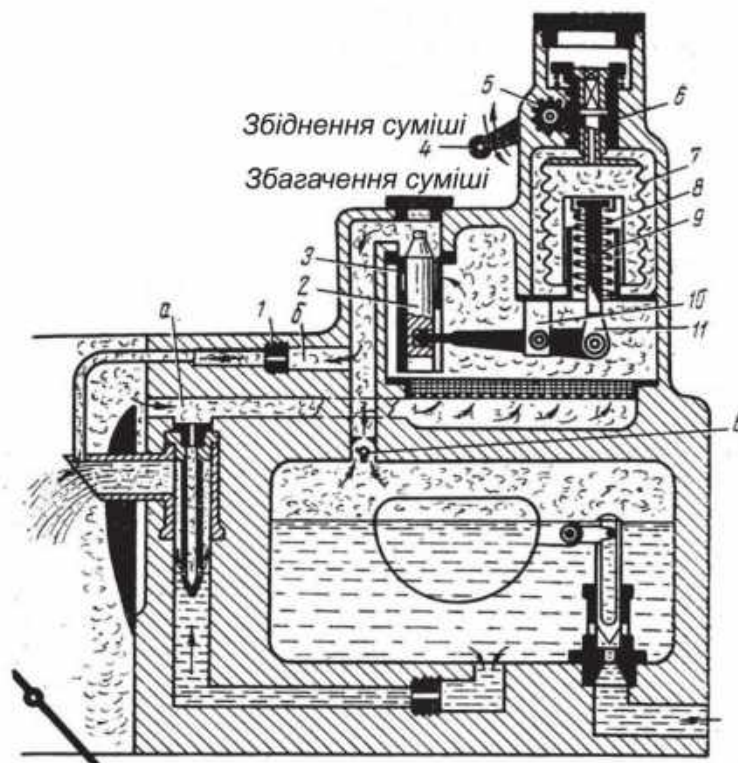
Схема та принцип дії висотного коректора: 1 – повітряний жиклер; 2 – голка; 3 – гніздо голки; 4 – важіль механізму ручного керування; 5 – валик з шестірнею; 6 – рейка; 7 – анероїд; 8 – пружина; 9 – тяга; 10 – опорна пластина; 11 – двоплечовий важіль; а – канал для сполучення внутрішньої порожнини коректора із задифузурним простором; б – обвідний канал; в – відгалуження обвідного каналу
